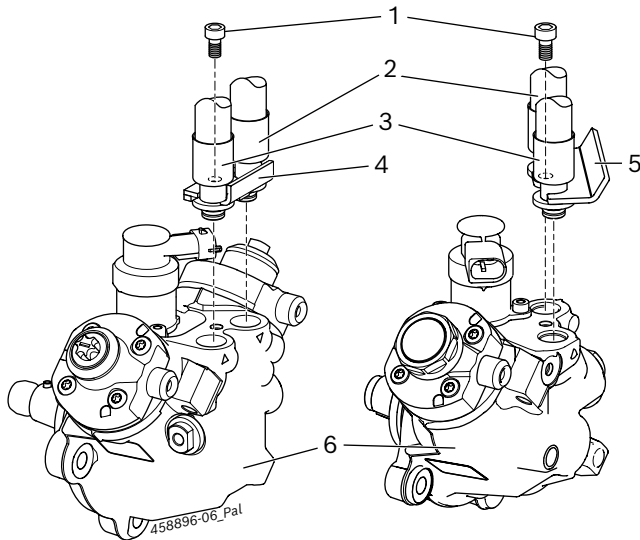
Prüfanschluss CP4 mit Haltewinkel
